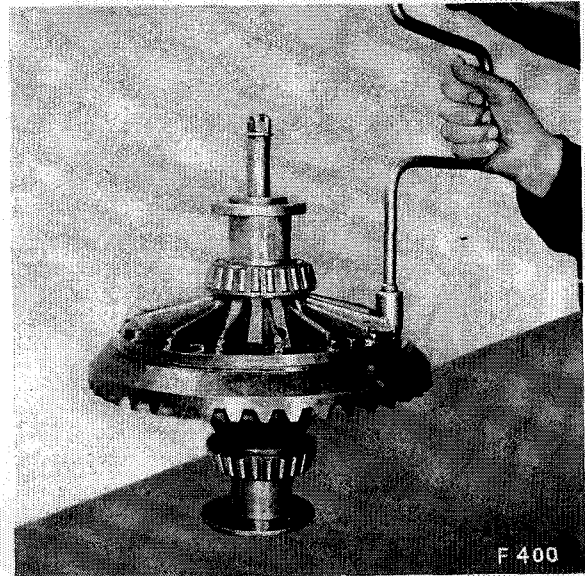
Lösen der Schrauben zur Befestigung des Tellerrades
